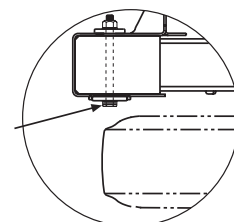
Installation alternative du boulon de pivot QUIK-ALIGN
